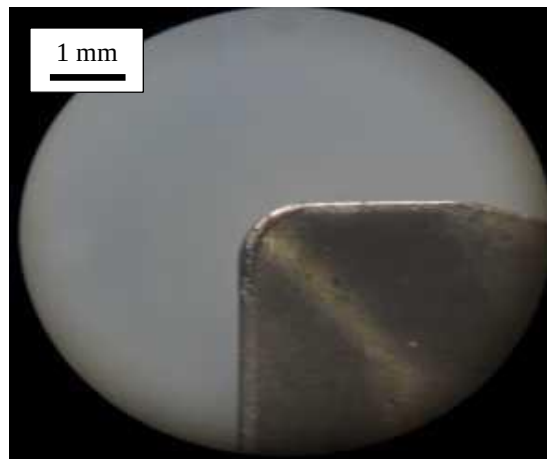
Inserto intercambiável de metal-duro após o Processo de Usinagem por Fresamento – condição: “usado”.
